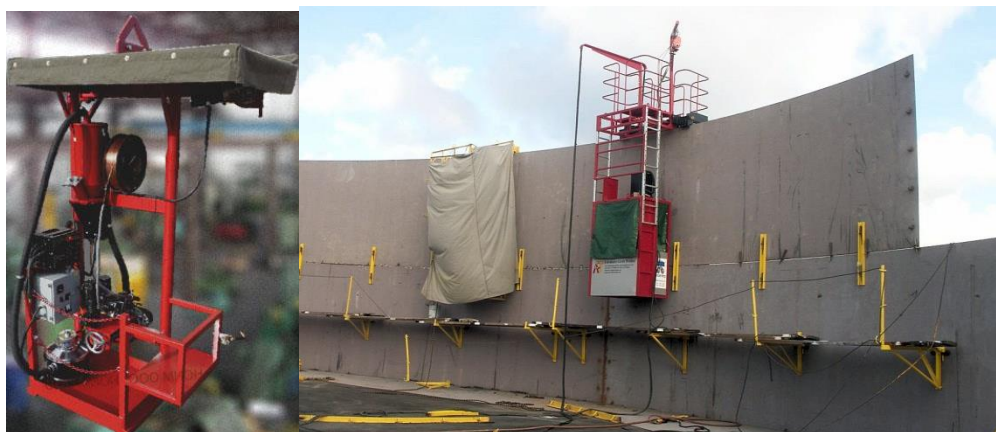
Установка AGW-I для сварки кольцевых швов резервуара
